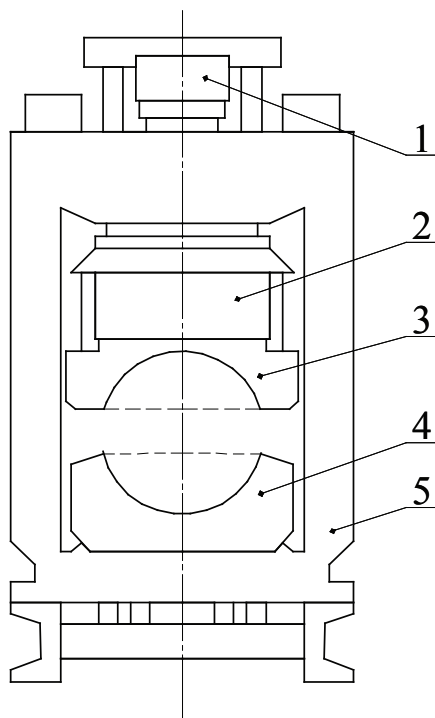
Схема прессы для окончательной формовки трубной заготовки:
